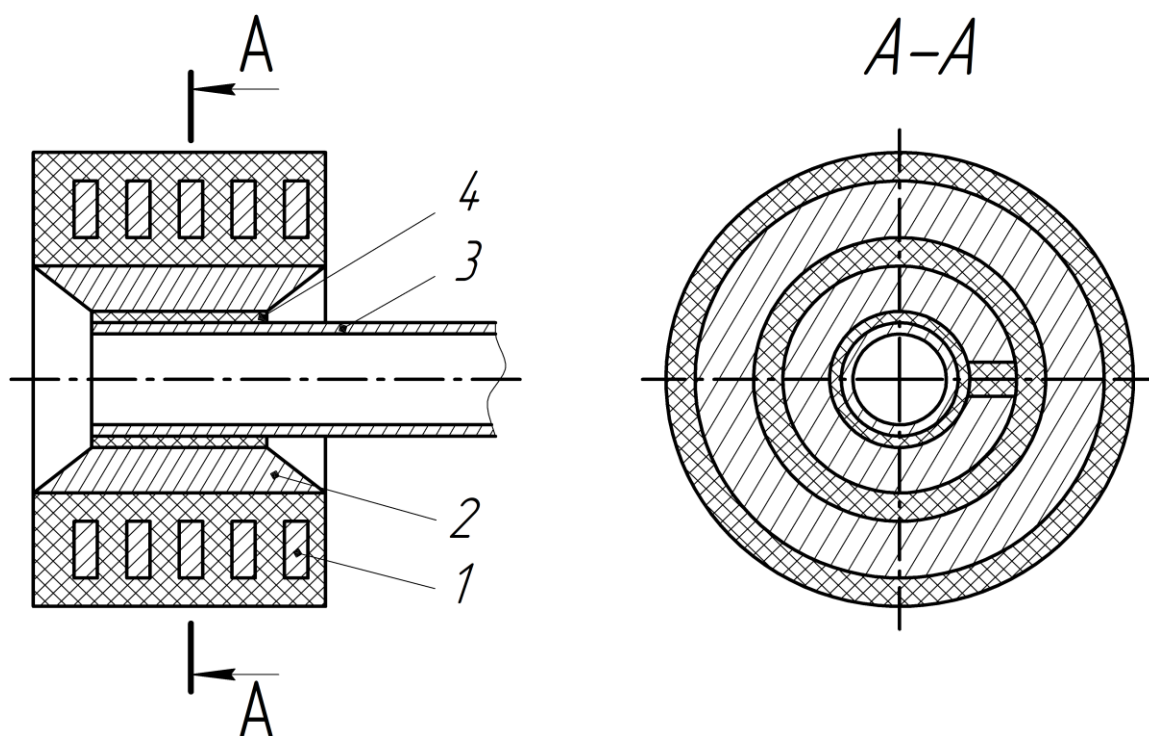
Індуктор для обтиснення трубчастої заготовки: 1 – спіраль індуктора; 2 – концентратор магнітного поля; 3 – трубчаста заготовка; 4 – ізоляційна втулка
